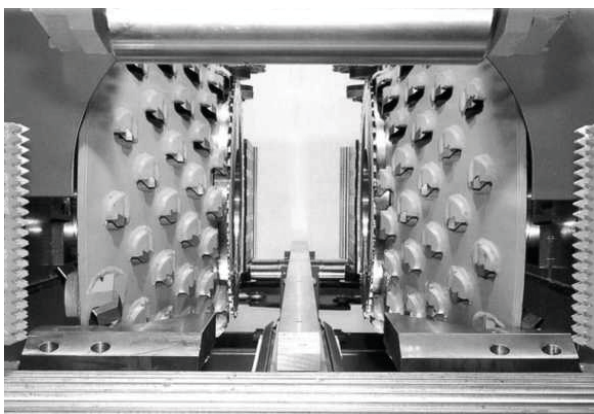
Сборные фрезы фрезерно-брусующих станков
